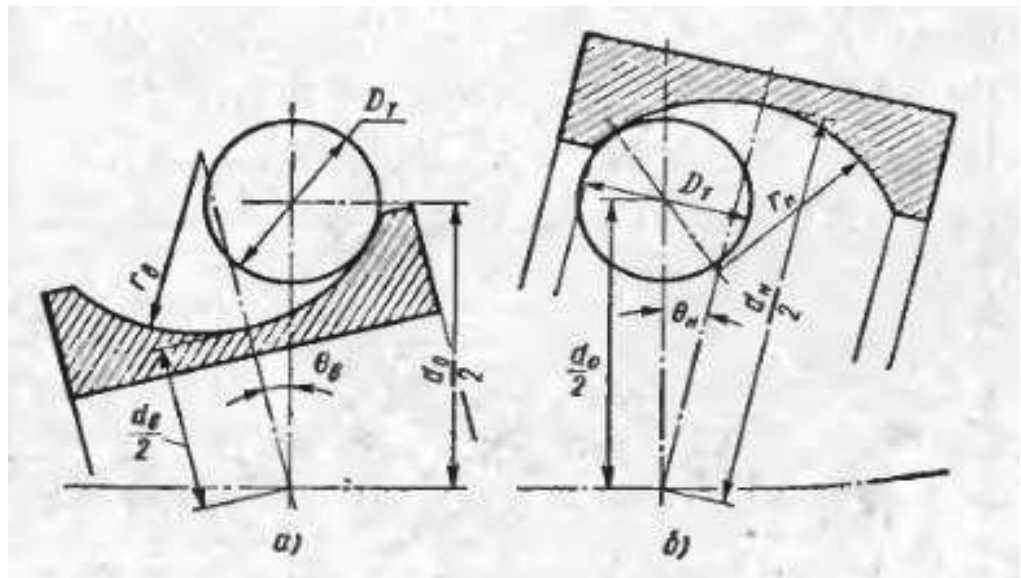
Расчетная схема определения допускаемого угла перекоса
